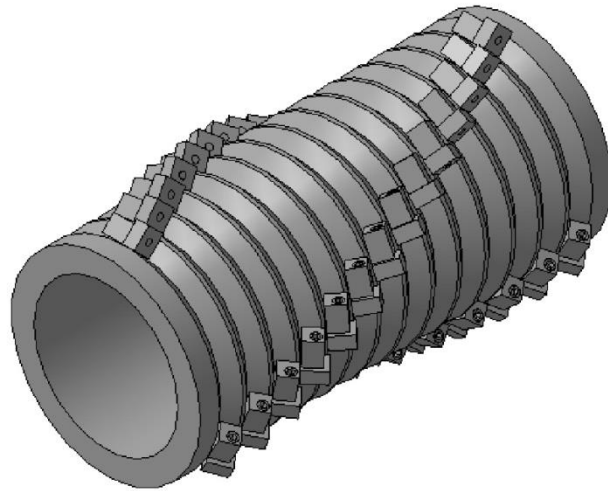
3D модель барабана F-Rotor з різальними пластинами
